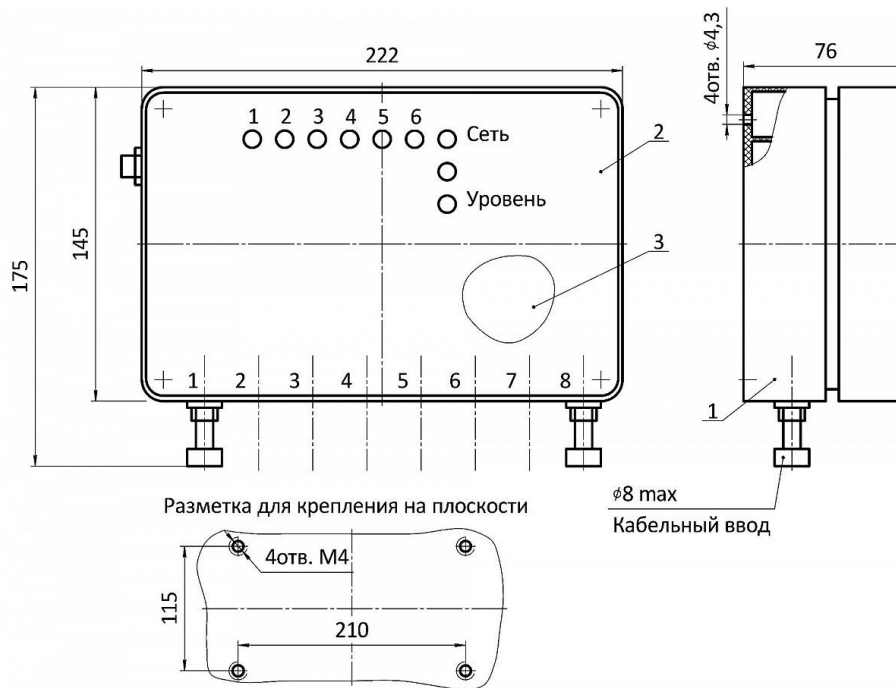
Габаритные и установочные размеры преобразователя передающего ППР-6, ППР-6И
